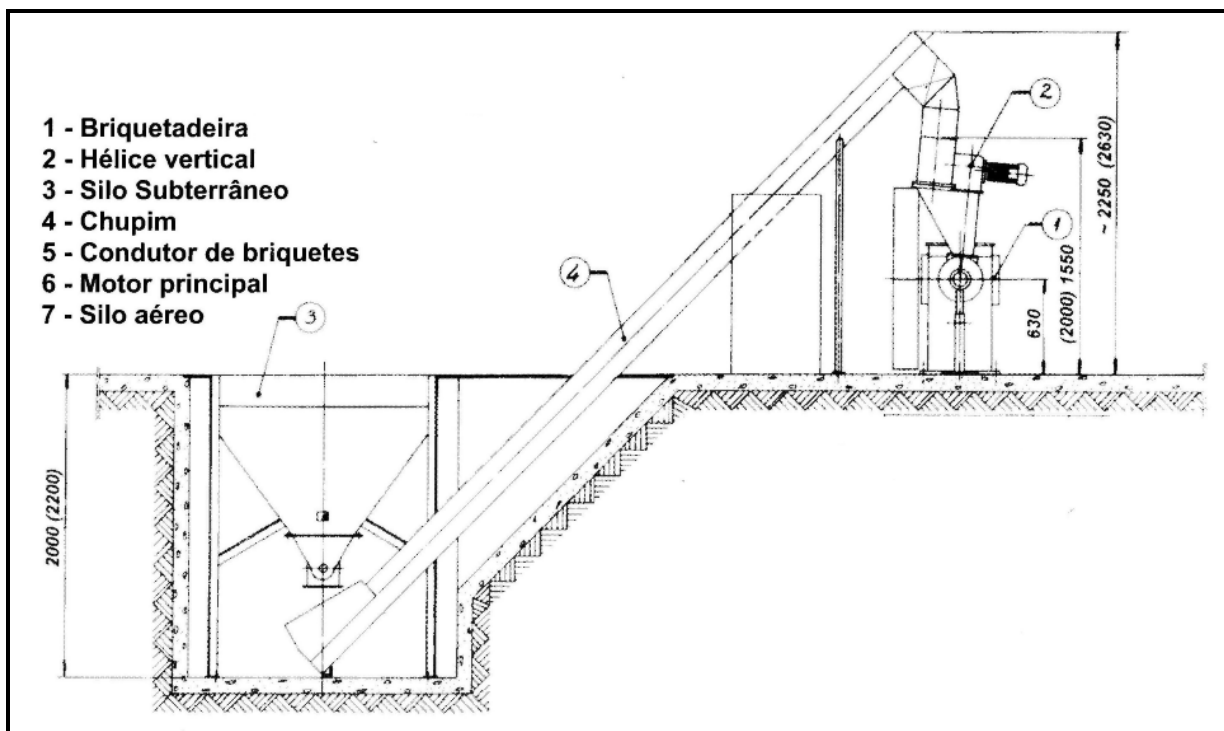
Vista lateral do sistema de abastecimento da briquetadeira.
